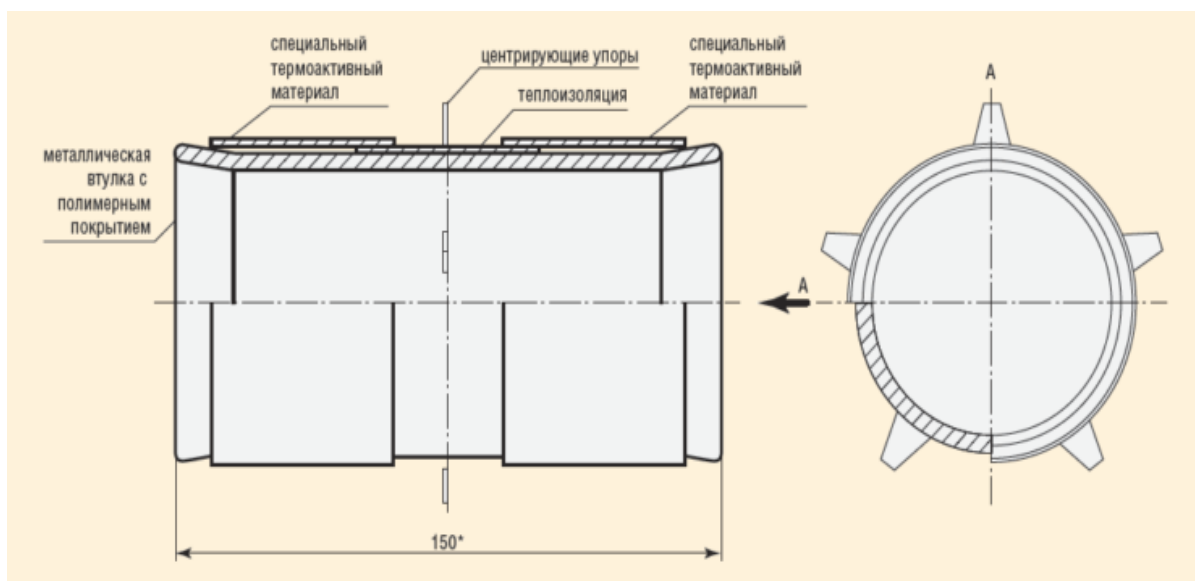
Схема узла сварного соединения с CPS-штулкой
